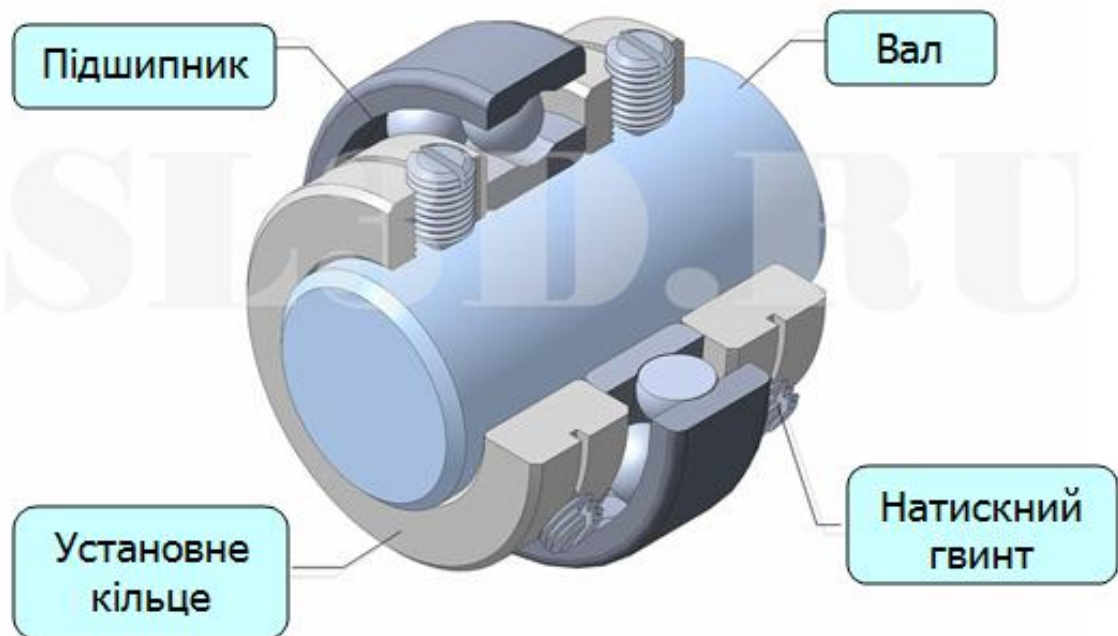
Установка підшипника установочними кільцями з натискними гвинтами.
